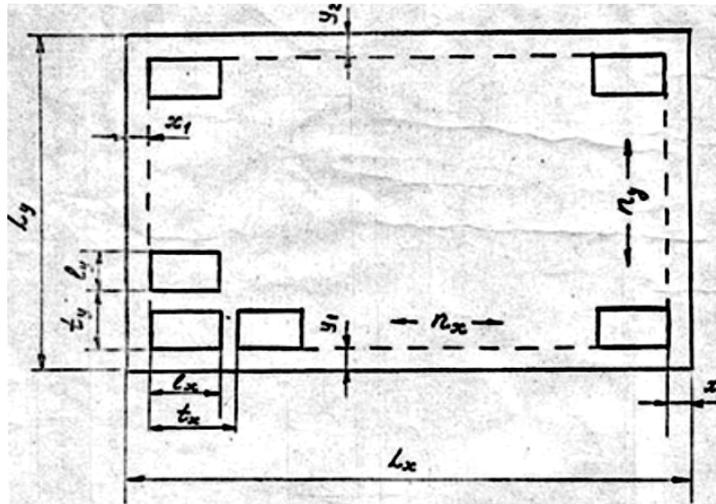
Схема расположения корпусированных ИС ШП на плате
